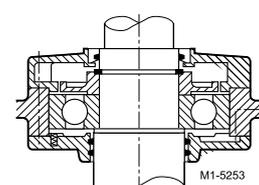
Rodamiento LA Rodamiento LA Rodamiento LCA
